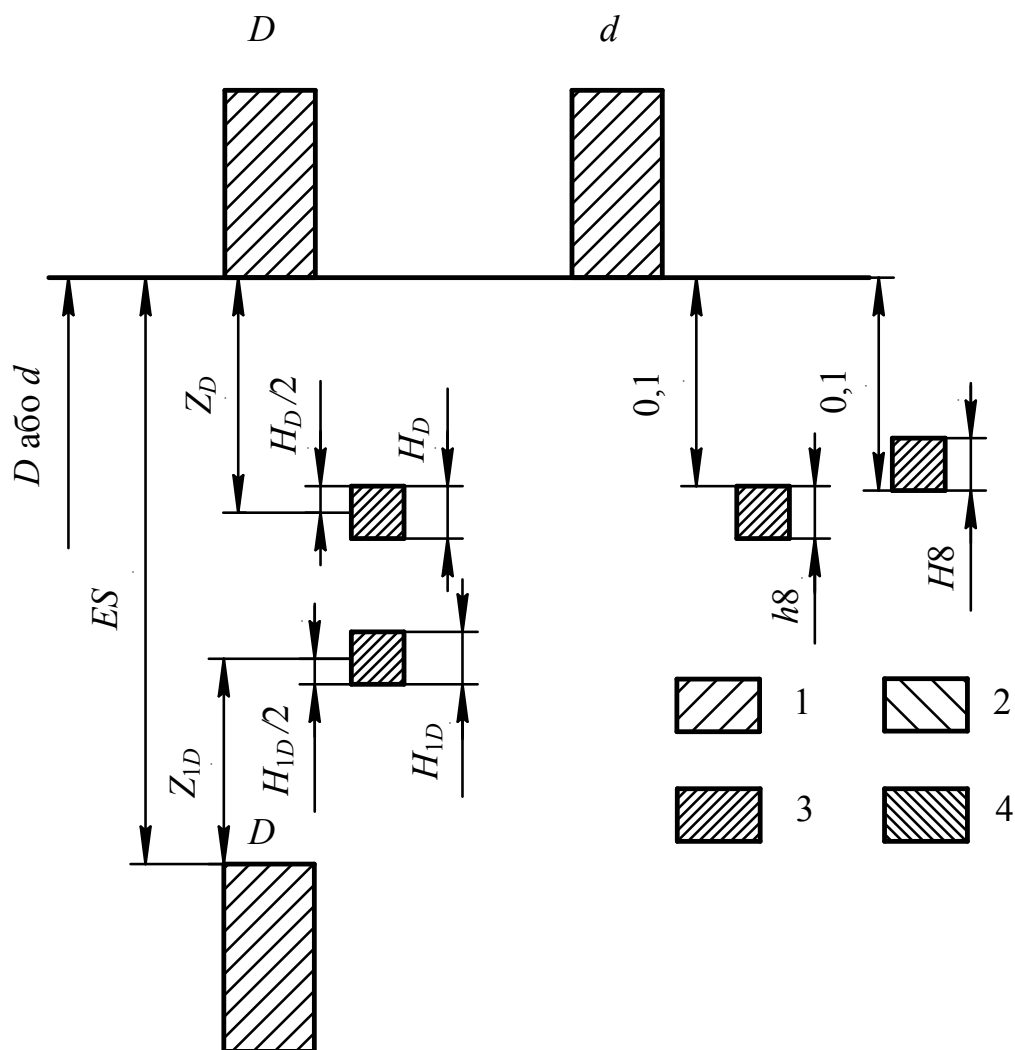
Розташування полів допусків: 1 - діаметра D або d втулки, що не центрують; 2 - діаметра D вала, що не центрує; 3 - на виготовлення калібра-пробки; 4 - на виготовлення калібра-кільця
